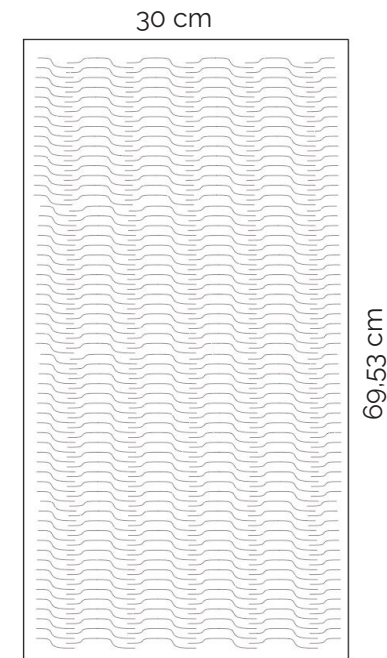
Dimensiones y cortes de kerf bending para pieza interna con material. Elaboración propia.
